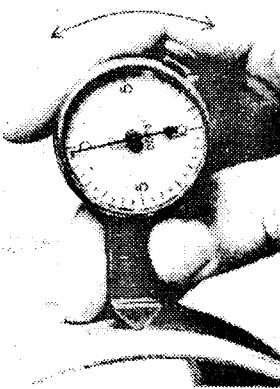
Калибр с уравновешенным циферблатом, приложенный к резьбе и показывающий небольшую погрешность в высоте резьбы
